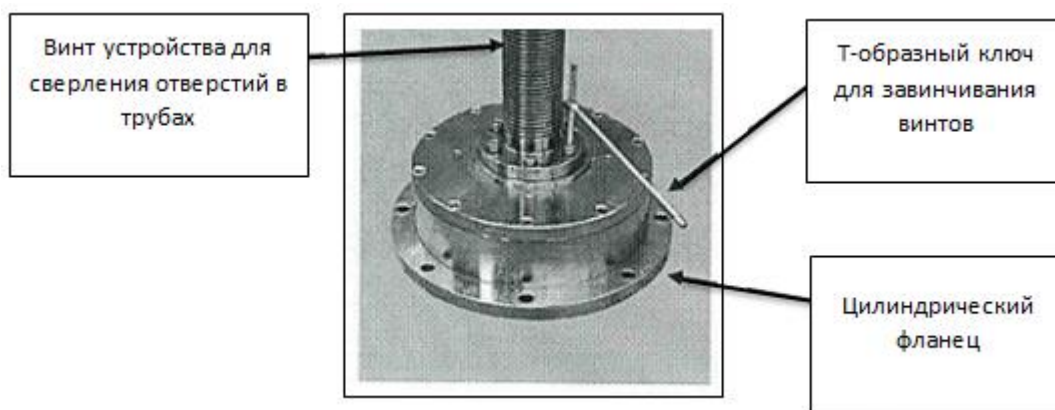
Установка рабочего винта на цилиндрический фланец
